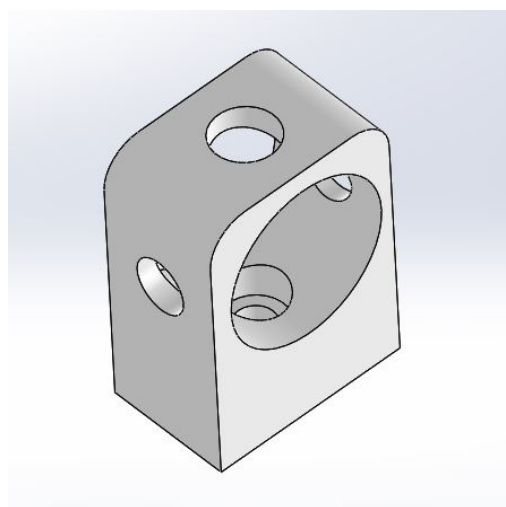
Soporte del actuador lineal (Fuente: propia)
